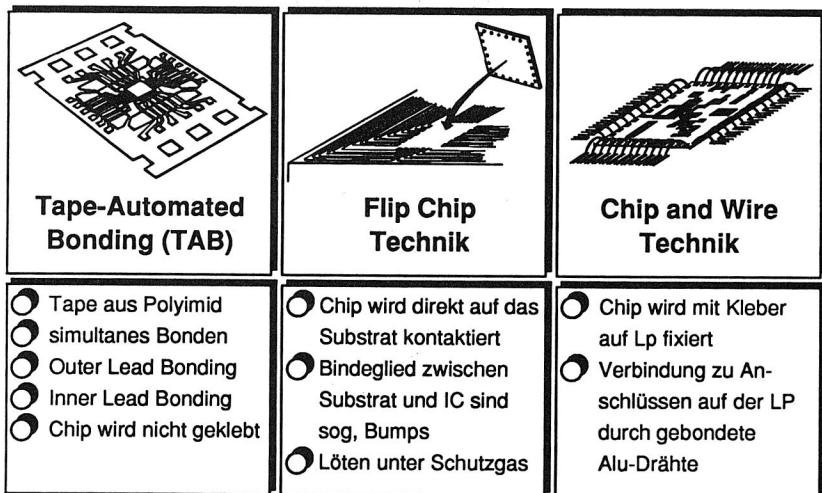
Montagevarianten zur Verarbeitung ungehäuseter Chips
